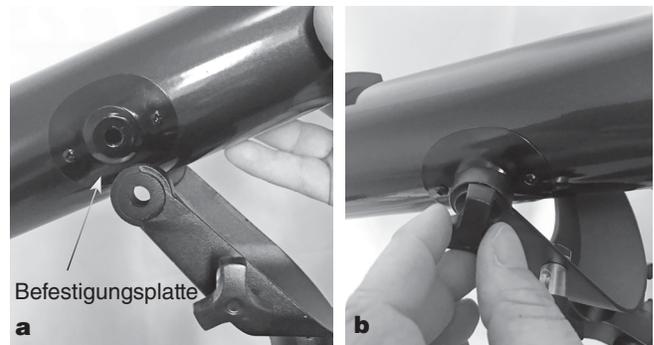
a) Platzieren Sie das Optiktrohr in der Gabelmontierung, wobei die Bohrungen der Befestigungsplatten auf denen der Gabelmontierung liegen müssen. b) Schrauben Sie die Arretierschraube der Gabelmontierung in die Gewindebohrungen der Befestigungsplatten.
